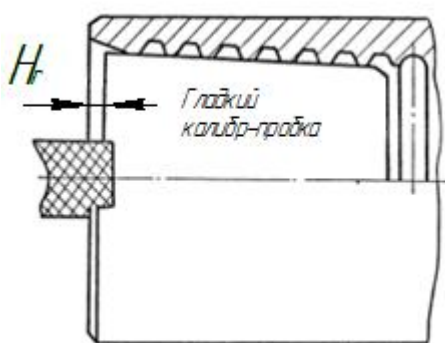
Схема контроля натяга резьбы муфт гладким калибром – пробкой
